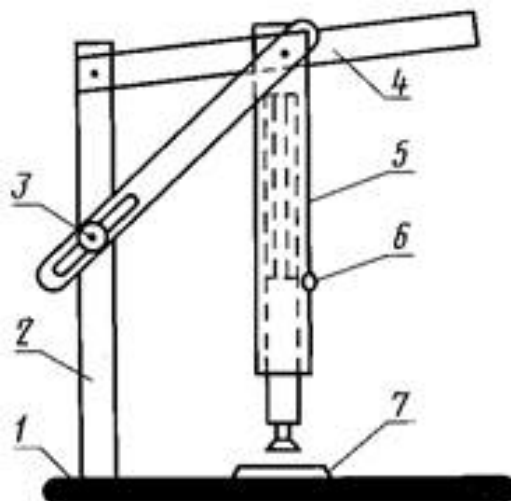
Приспособление для создания нагрузки: 1 – основание; 2 – стойка; 3 – установочный винт; 4 – рычаг; 5 – гильза с винтовой пружиной; 6 – контрольная отметка; 7 – пластинка для испытания
